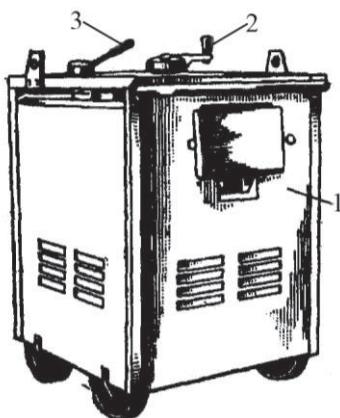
Сварочный трансформатор ТД-500: 1 – корпус; 2 – ручка ходового винта; 3 – переключатель ступеней
